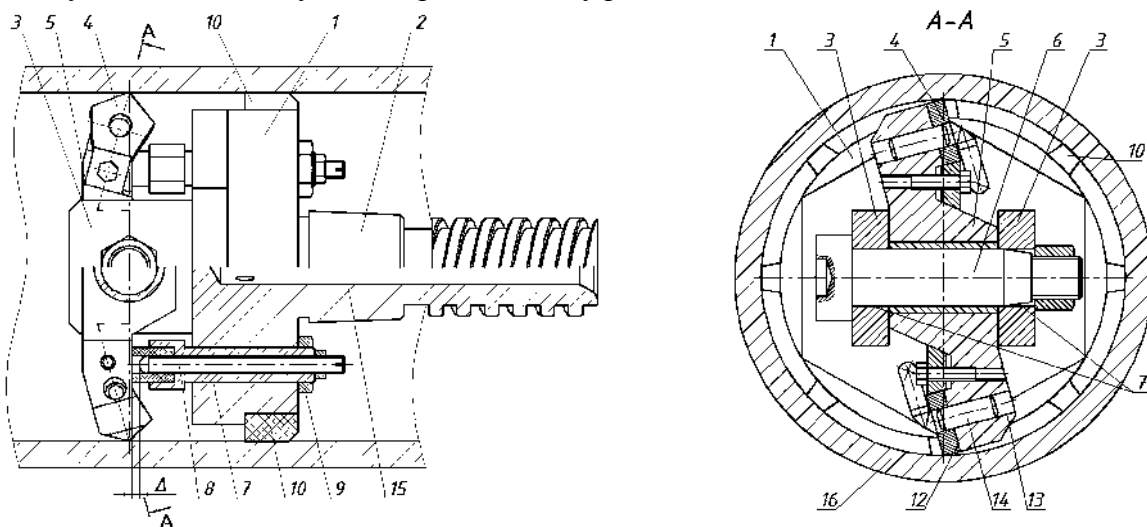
Схема дворізнцевої адаптивної розточної головки
